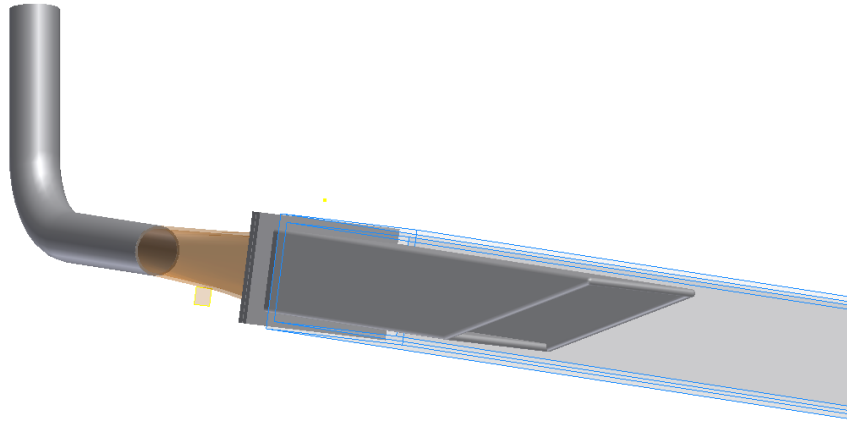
CAD-Zeichnung des Tauchrohrs mit rechteckigem Querschnitt
